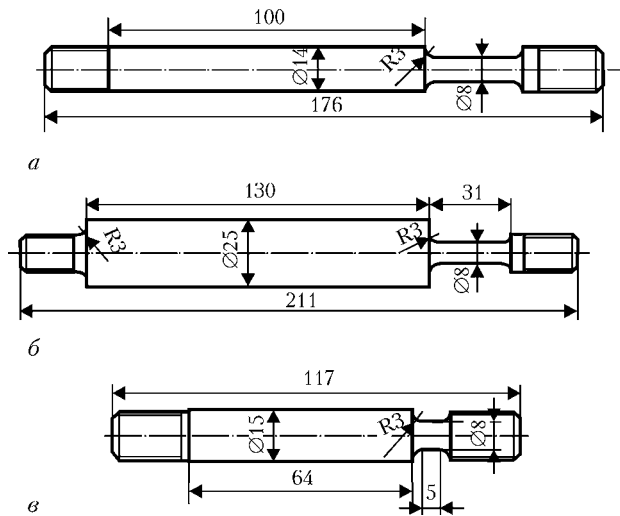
Схемы образцов для испытаний: а — из нержавеющей стали; б — из низкоуглеродистой стали 20; в — из армо-железа
